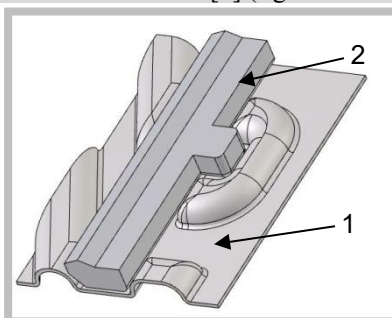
sezione piastra di scambio calore [1] con guarnizione installata [2]
